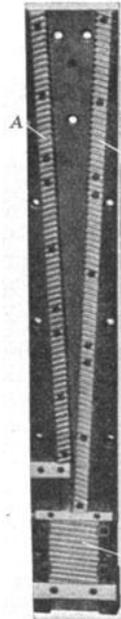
Räumzeug zur Bearbeitung roher Gußflächen eines Räderkastens.
